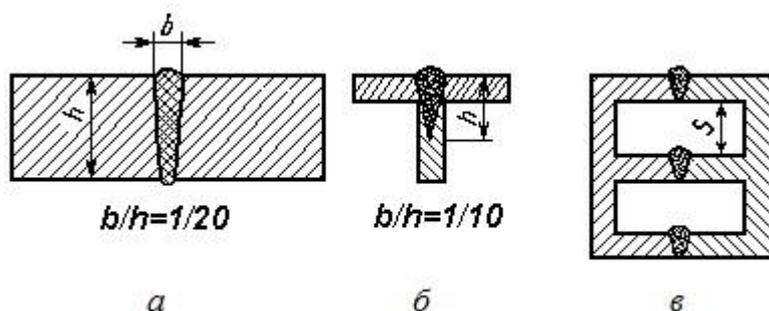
Типы сварных соединений, выполняемых электронно-лучевой сваркой
